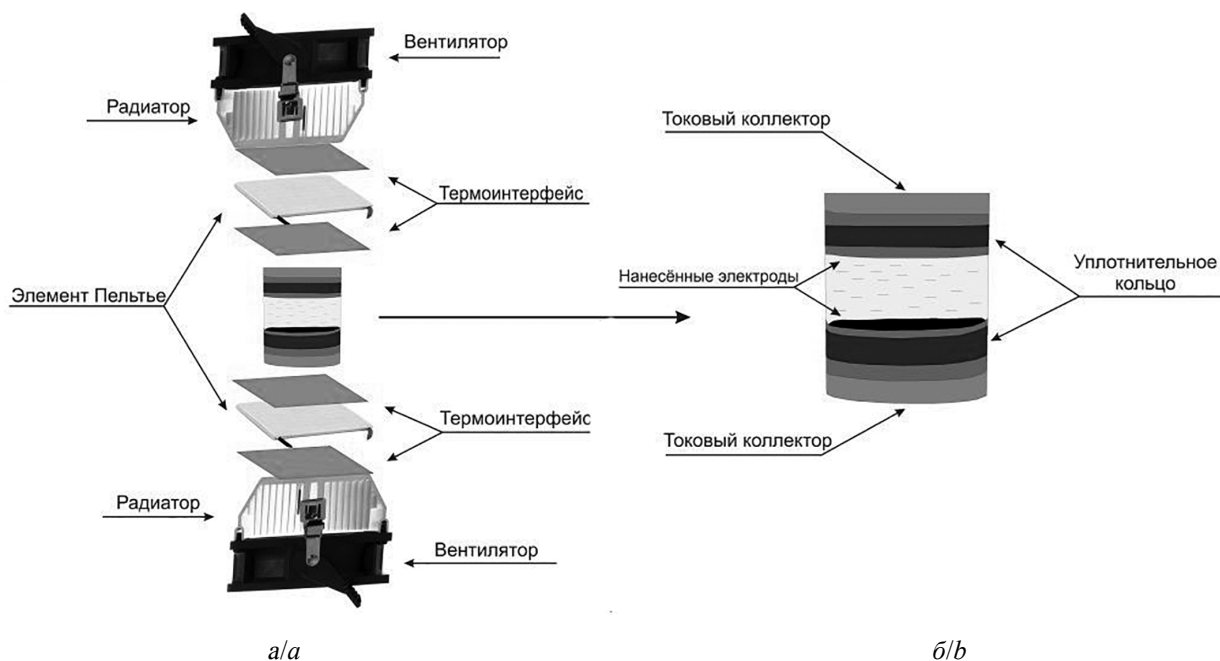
Схема сборки конструкции для нагрева и охлаждения ТЭХ (а) и схематическое изображение ТЭХ (б)
